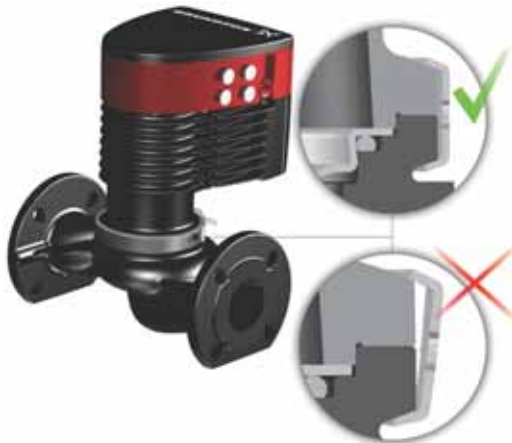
Instalación del cabezal de la bomba en la carcasa de la bomba
